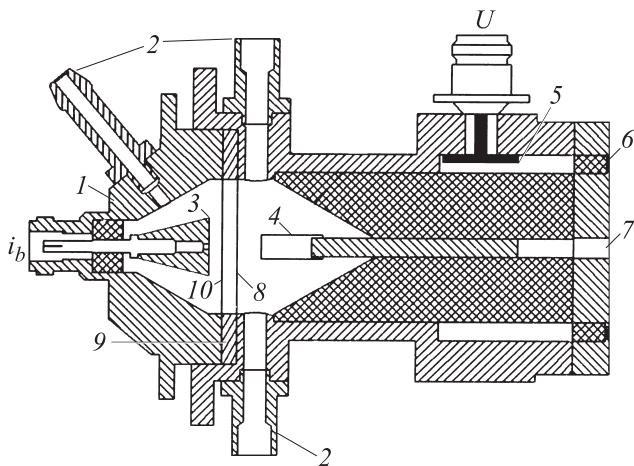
Сборочный чертеж разрядной камеры: 1 — корпус коллектора, 2 — патрубки для напуска и откачки газа, 3 — приемная часть коллектора, 4 — трубчатый катод, 5 — емкостной делитель напряжения, 6 — шунт, 7 — отверстие для подключения высоковольтного кабеля, 8 — анод из сетки, 9 — металлическое кольцо толщиной 2 мм, 10 — экранная сетка.
